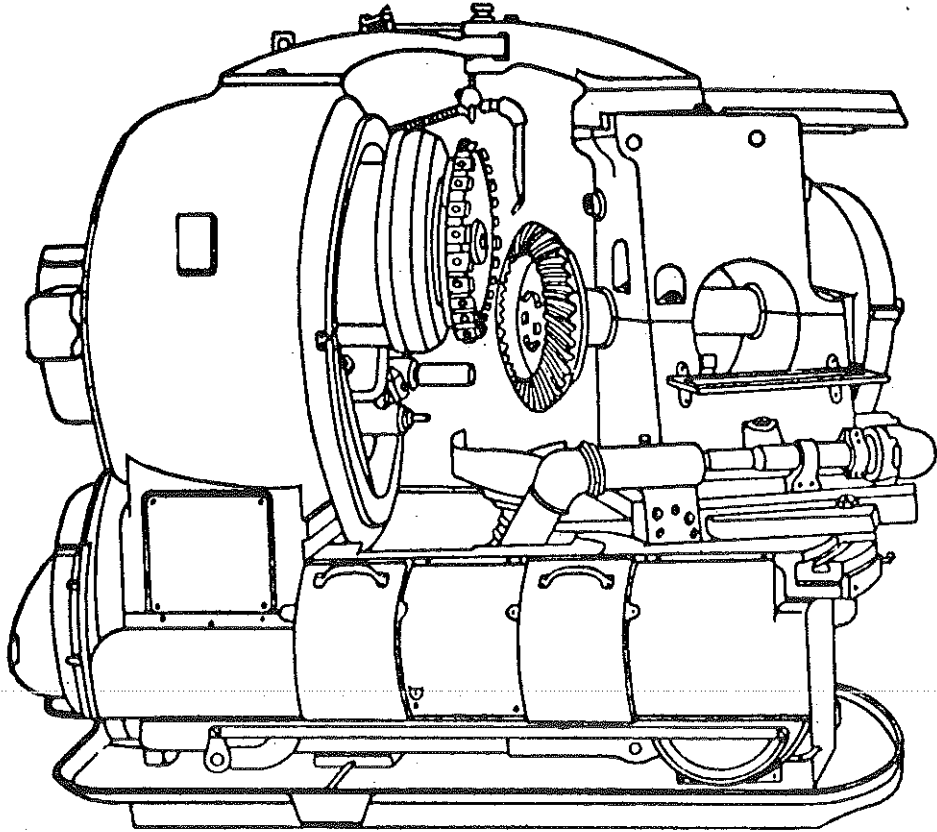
Denteadora Gleason para engrenagens cônicas.
